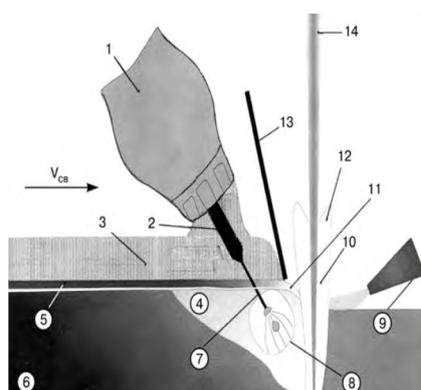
Схема гибридной лазерно-дуговой сварки под флюсом
